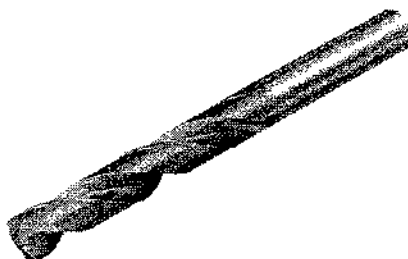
Сверло 460.1-0404-020A1-ХМ
